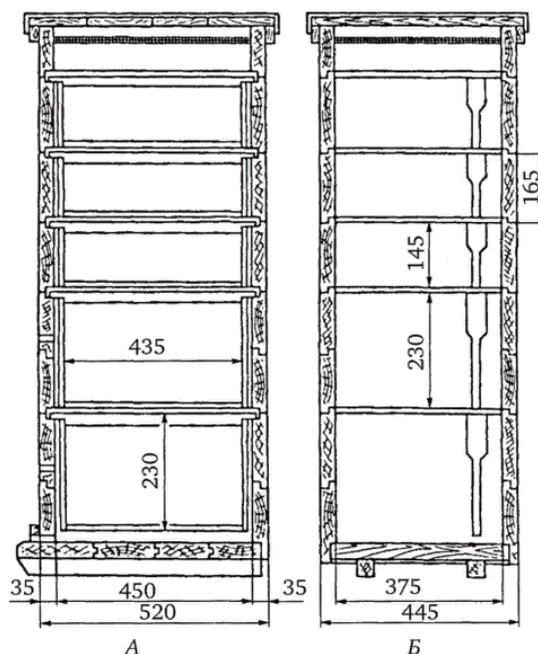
Двухкорпусный улей с магазинными надставками:
